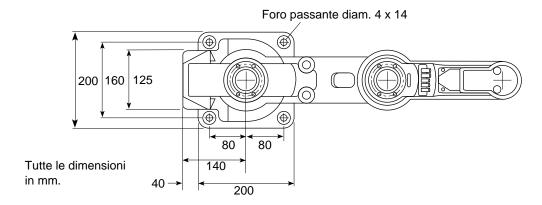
Percorso del foro di montaggio (tra robot e superficie di montaggio)
